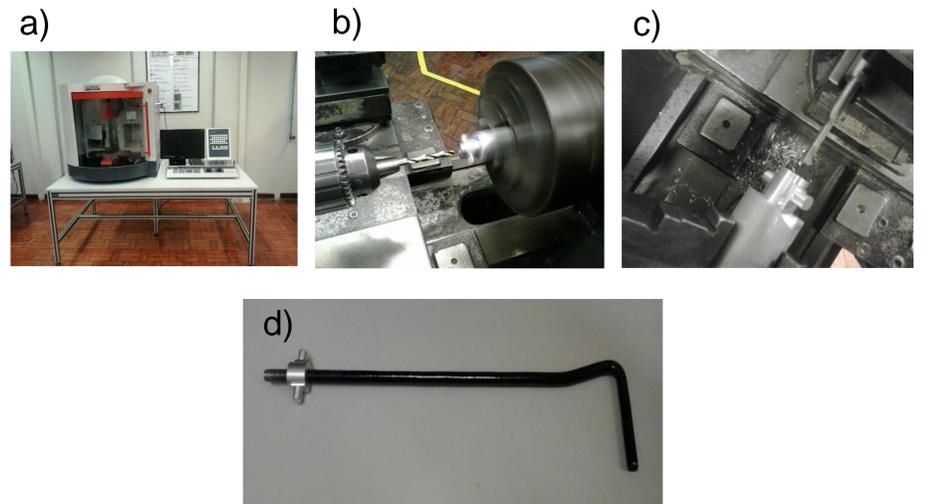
Centro de usinagem usado na usinagem do perfil externo(a) furação anterior ao rosqueamento (b) rosqueamento (c) e peça acabada montada (d).
